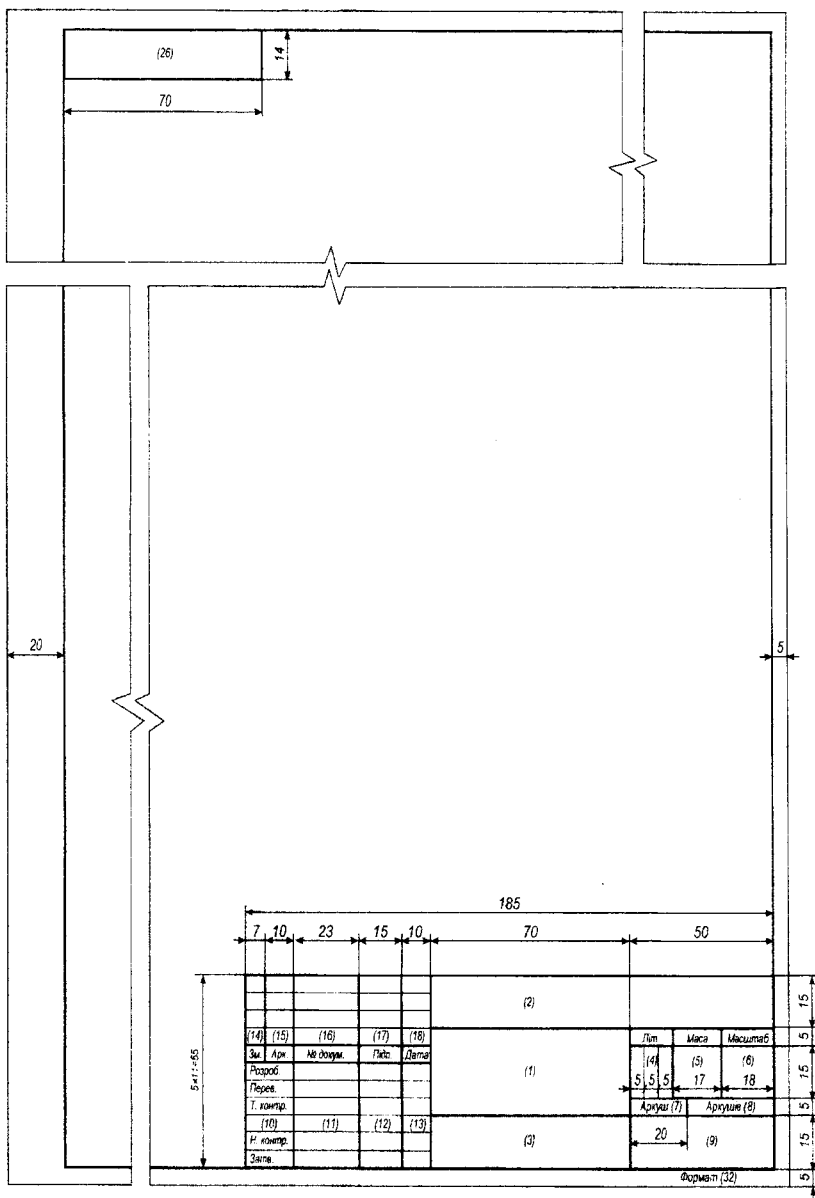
Основний напис конструкторських креслень і схем – форма 1
